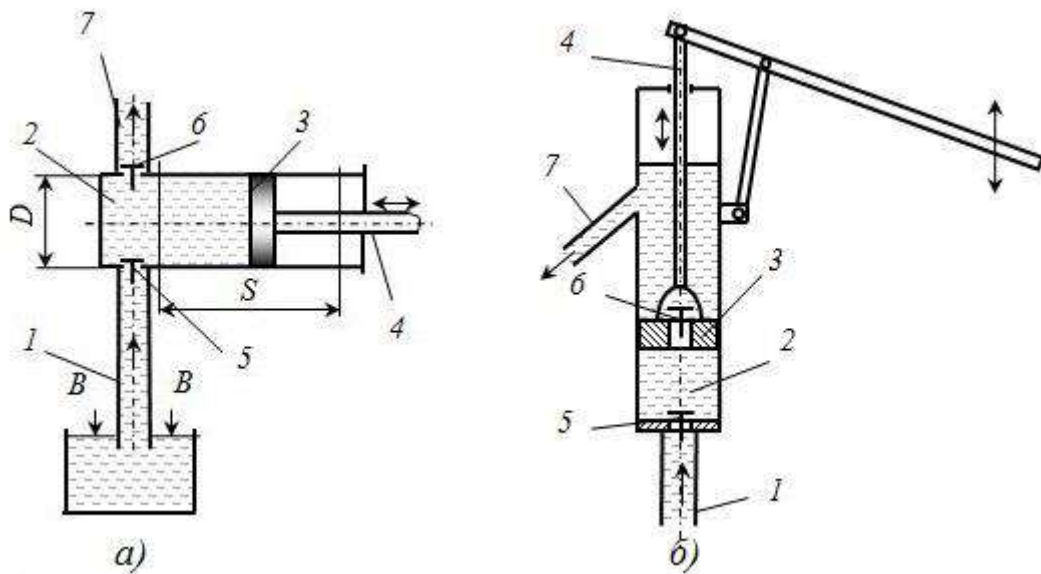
Схеми поршкових насосів: а – принципова схема; б – схема вертикального побутового насосу; 1 – всмоктувальний патрубок; 2 – робоча камера(циліндр); 3 – поршень; 4 – шток; 5,6 – відповідно впускний та випускний клапани; 7 – нагнітальний патрубок
